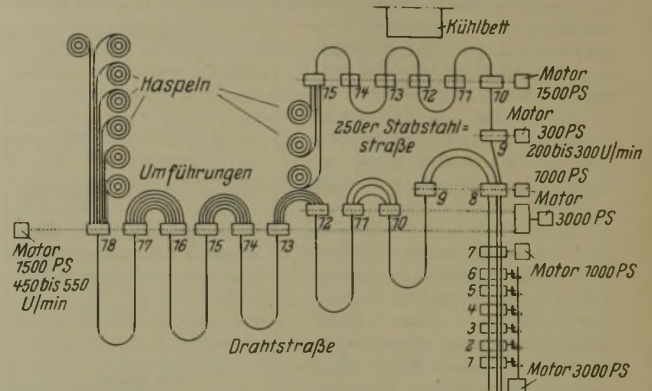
Walzplan, Antriebe und Gerüste der Drahtstraße und der 250er Stabstahlstraße.
